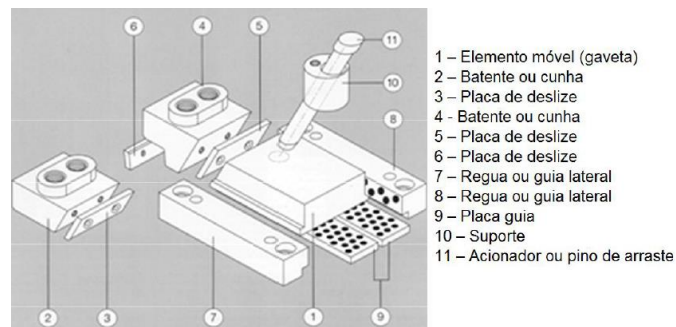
Vista explodida do mecanismo de elementos móveis [30]
